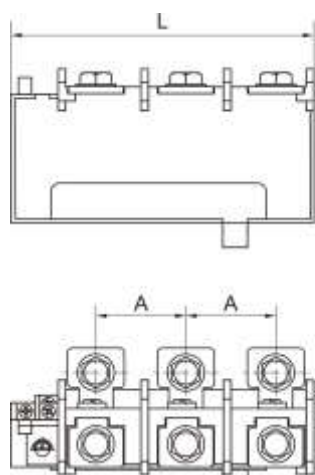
Габаритные и установочные размеры реле серии РТТ-325, РТТ-326, РТТ-327
